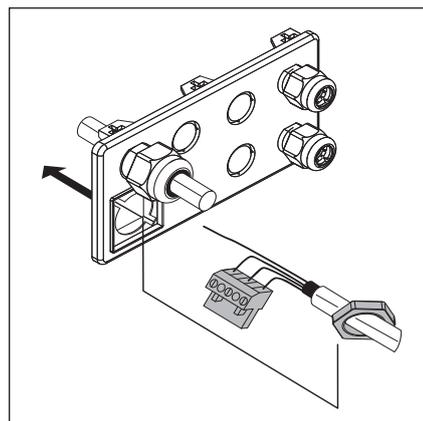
Stecker und Befestigungsmutter durch die Flanschplatte fädeln
